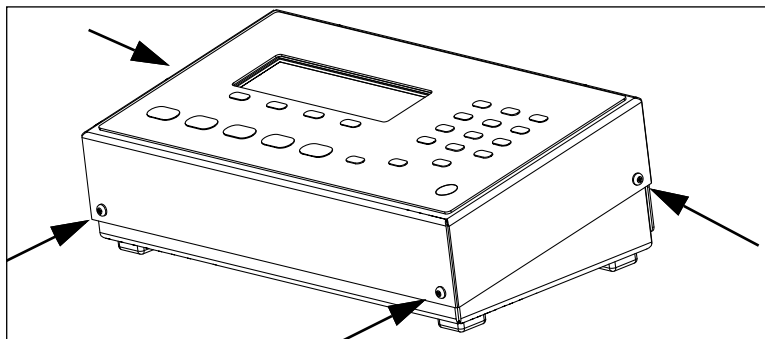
Tornillos de montaje de la cubierta de Counterpart
